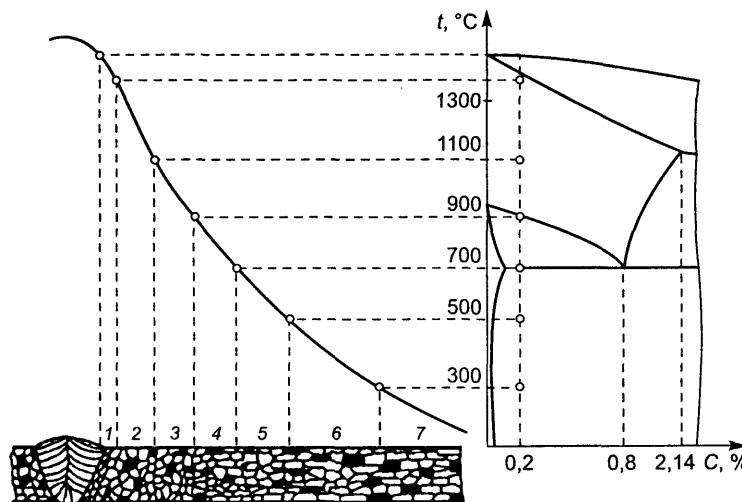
Схема строения зоны термического влияния сварного соединения при дуговой сварке низкоуглеродистой стали
